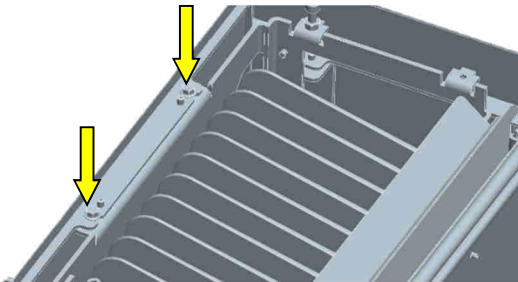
Befestigungsschrauben obere Frontblende lösen
